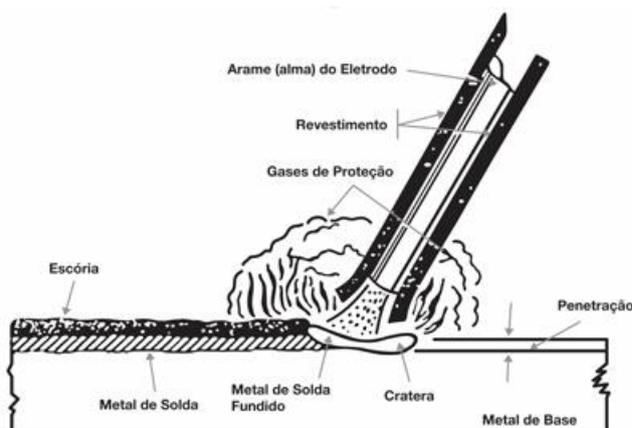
Processo de soldagem SMAW – Eletrodo revestido
